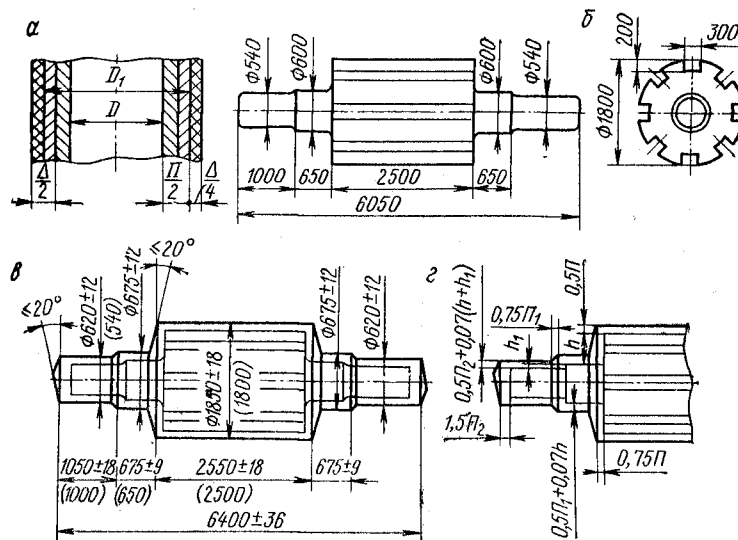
Пример составления чертежа поковки роторного вала, имеющего пазы дляковки на прессе:
